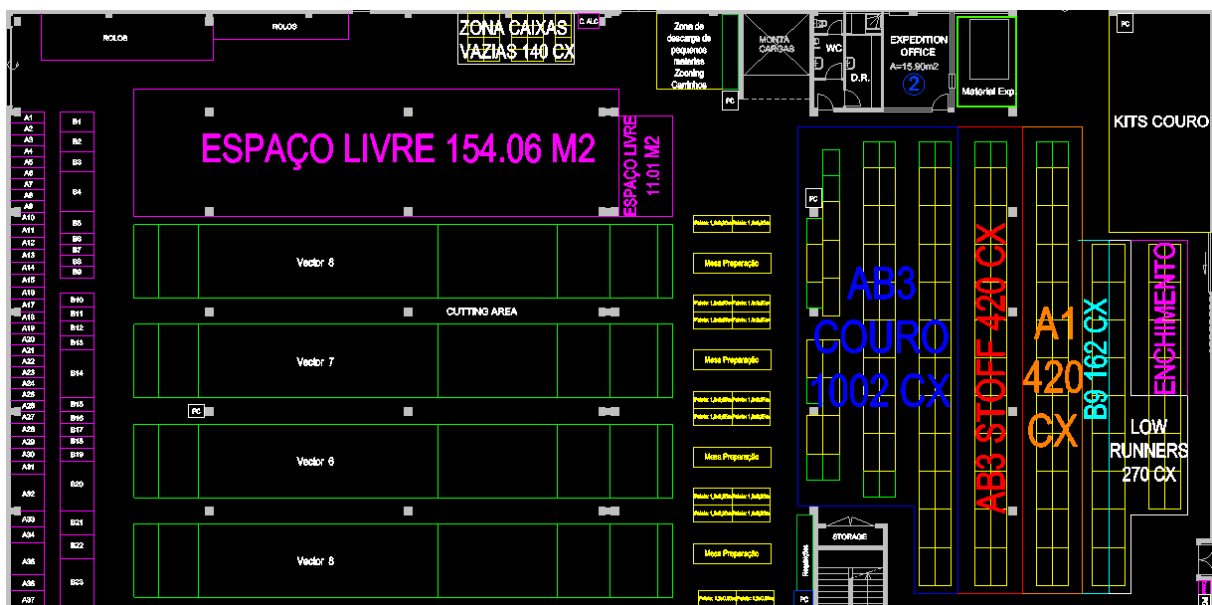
Segunda proposta layout futuro secção corte Joane I
